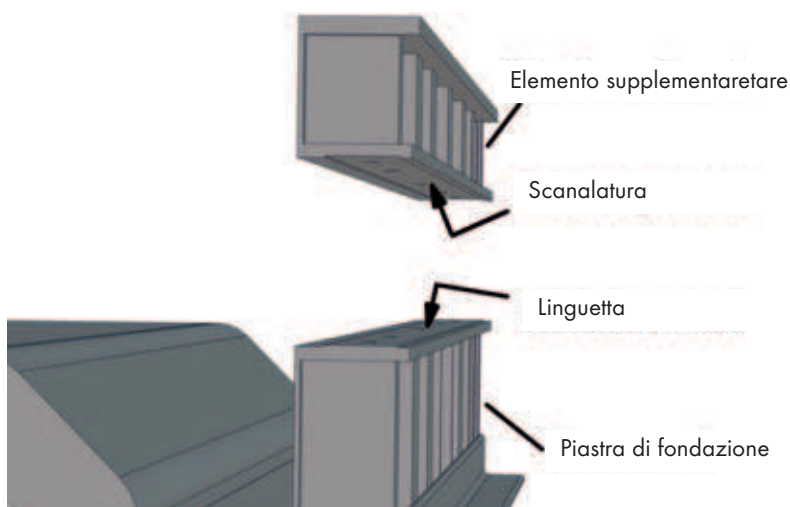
Parete laterale con piastra di fondazione ed elemento supplementare
